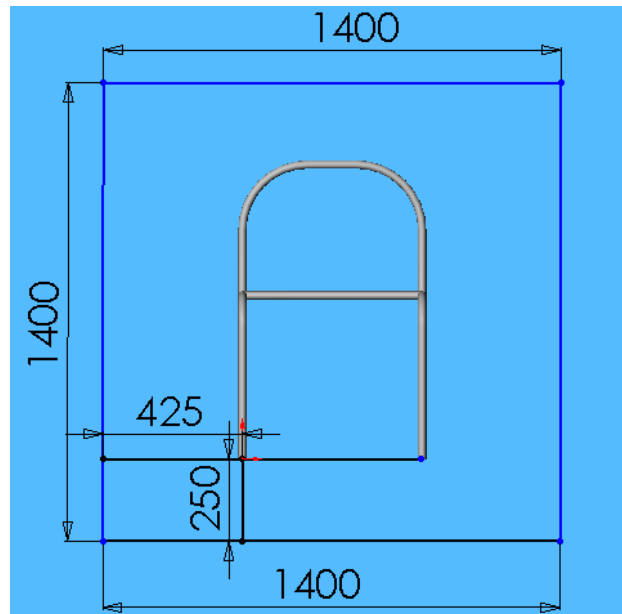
Dimensiones de la abertura de la cabina
